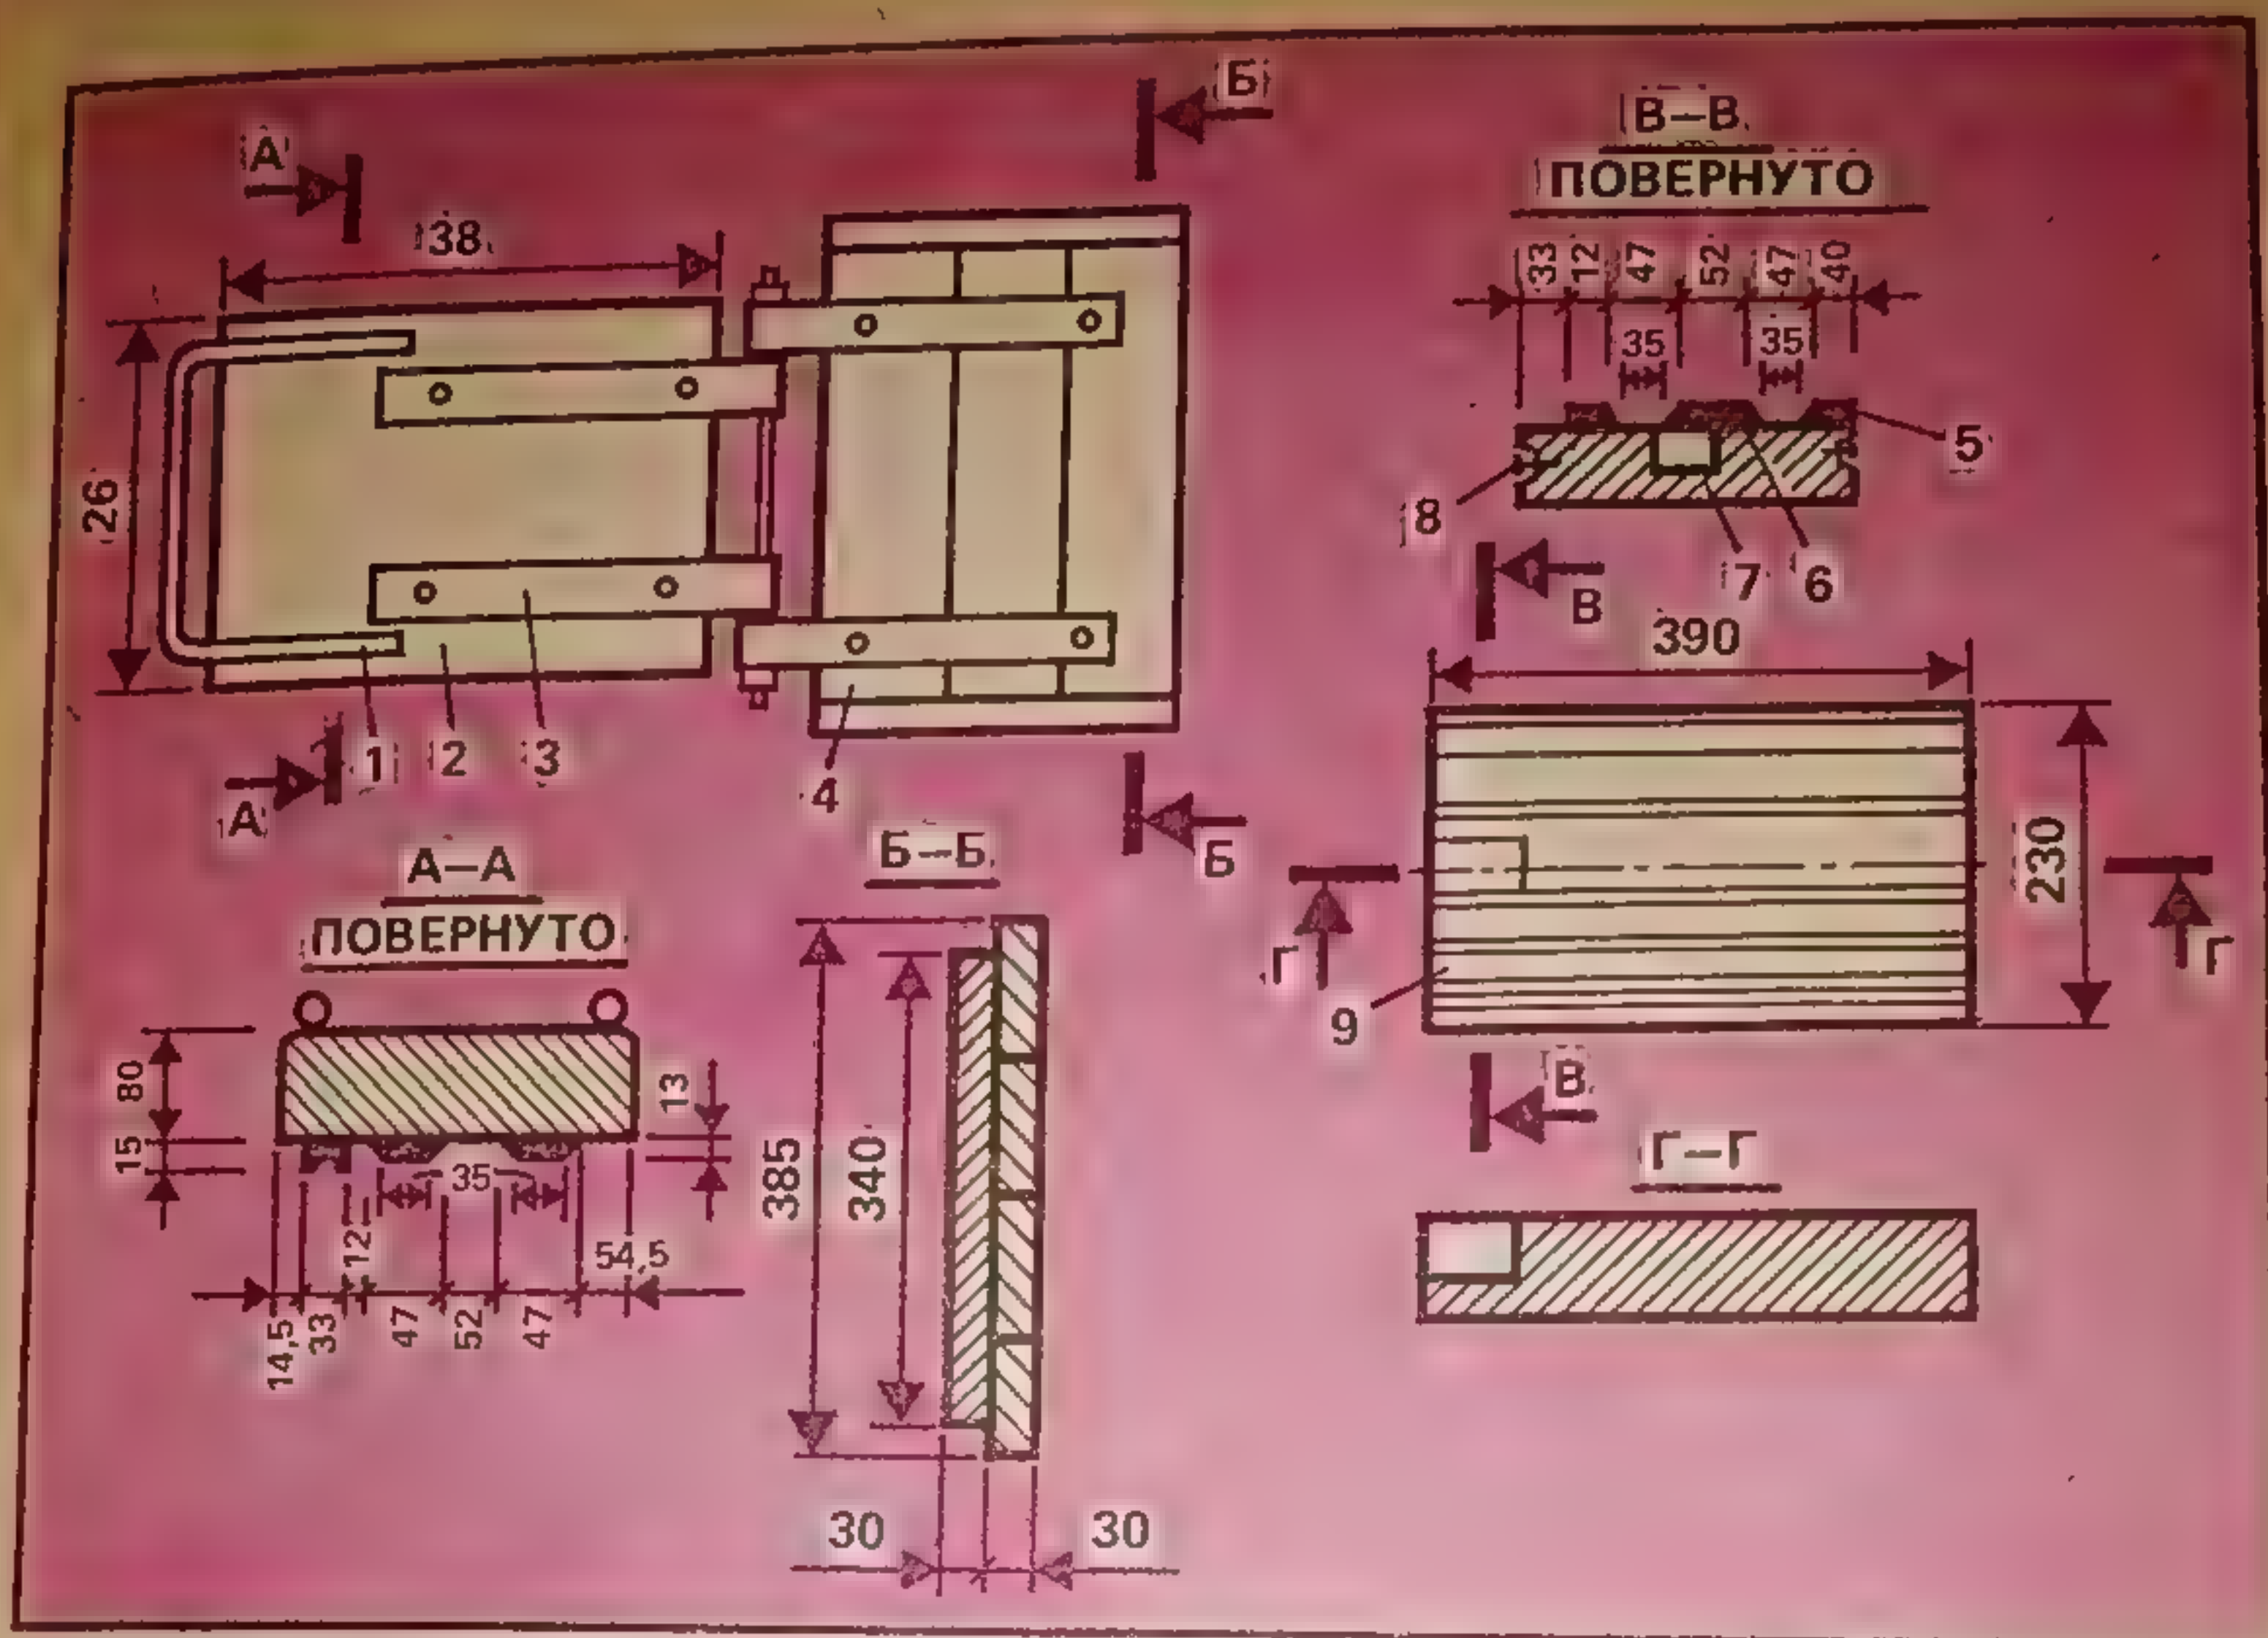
Формующие части под один из типов пазовой черепицы: 1 — рукоятка; 2 — пуансон; 3 — петля; 4 — направляющий щиток; 5 — металлическая окантовка; 6 — планка; 7 — основание; 8 — шуруп; 9 — матрица
